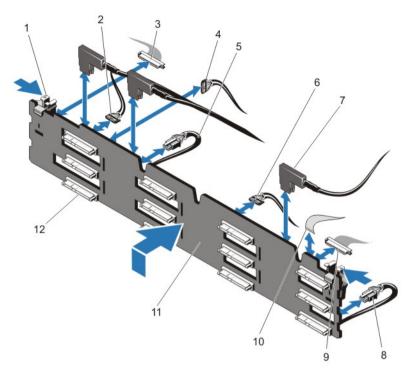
3,5-Zoll-SAS-Rückwandplatine (x12) entfernen und installieren
